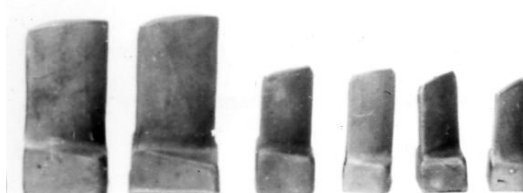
Номенклатура выдавленных заготовок лопаток из сплава ВТ8
